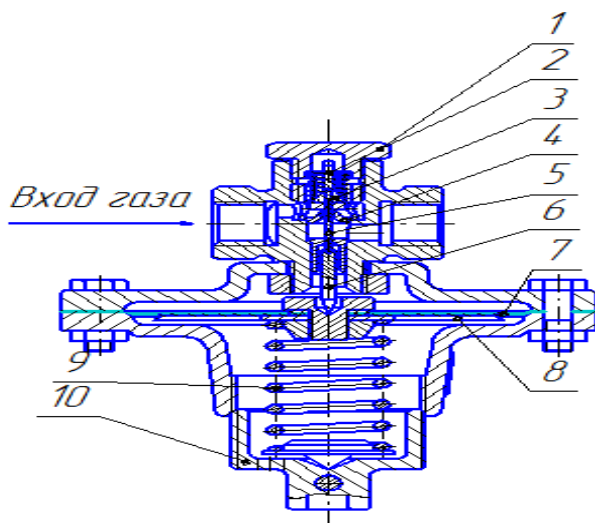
Регулятор управления: 1 – пробка; 2 – колпачок; 3 – клапан; 4 – седло клапана; 5 – шпилька; 6 – толкатель; 7 – мембрана; 8 – тарелка мембраны; 9 – регулировочная пружина; 10 – регулировочный стакан
